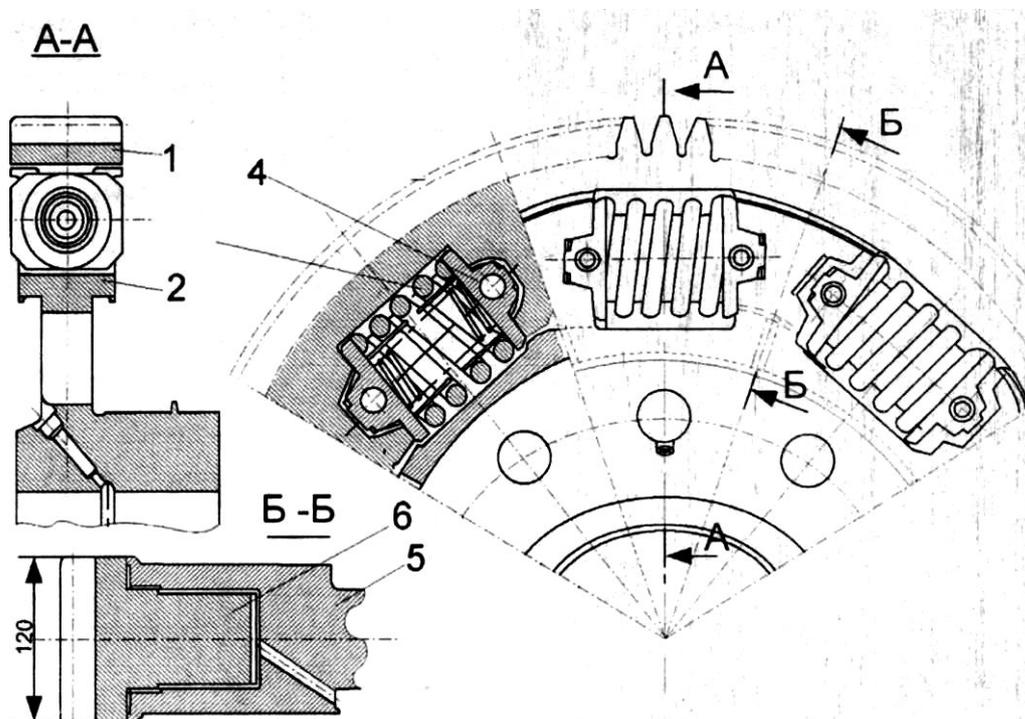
Зубчатое колесо электровоза Ф 1-венц; 2- центр зубчатого колеса; 3- пружины; 4-упоры; 5-выступы в центре зубчатого колеса; 6-выступы венца
